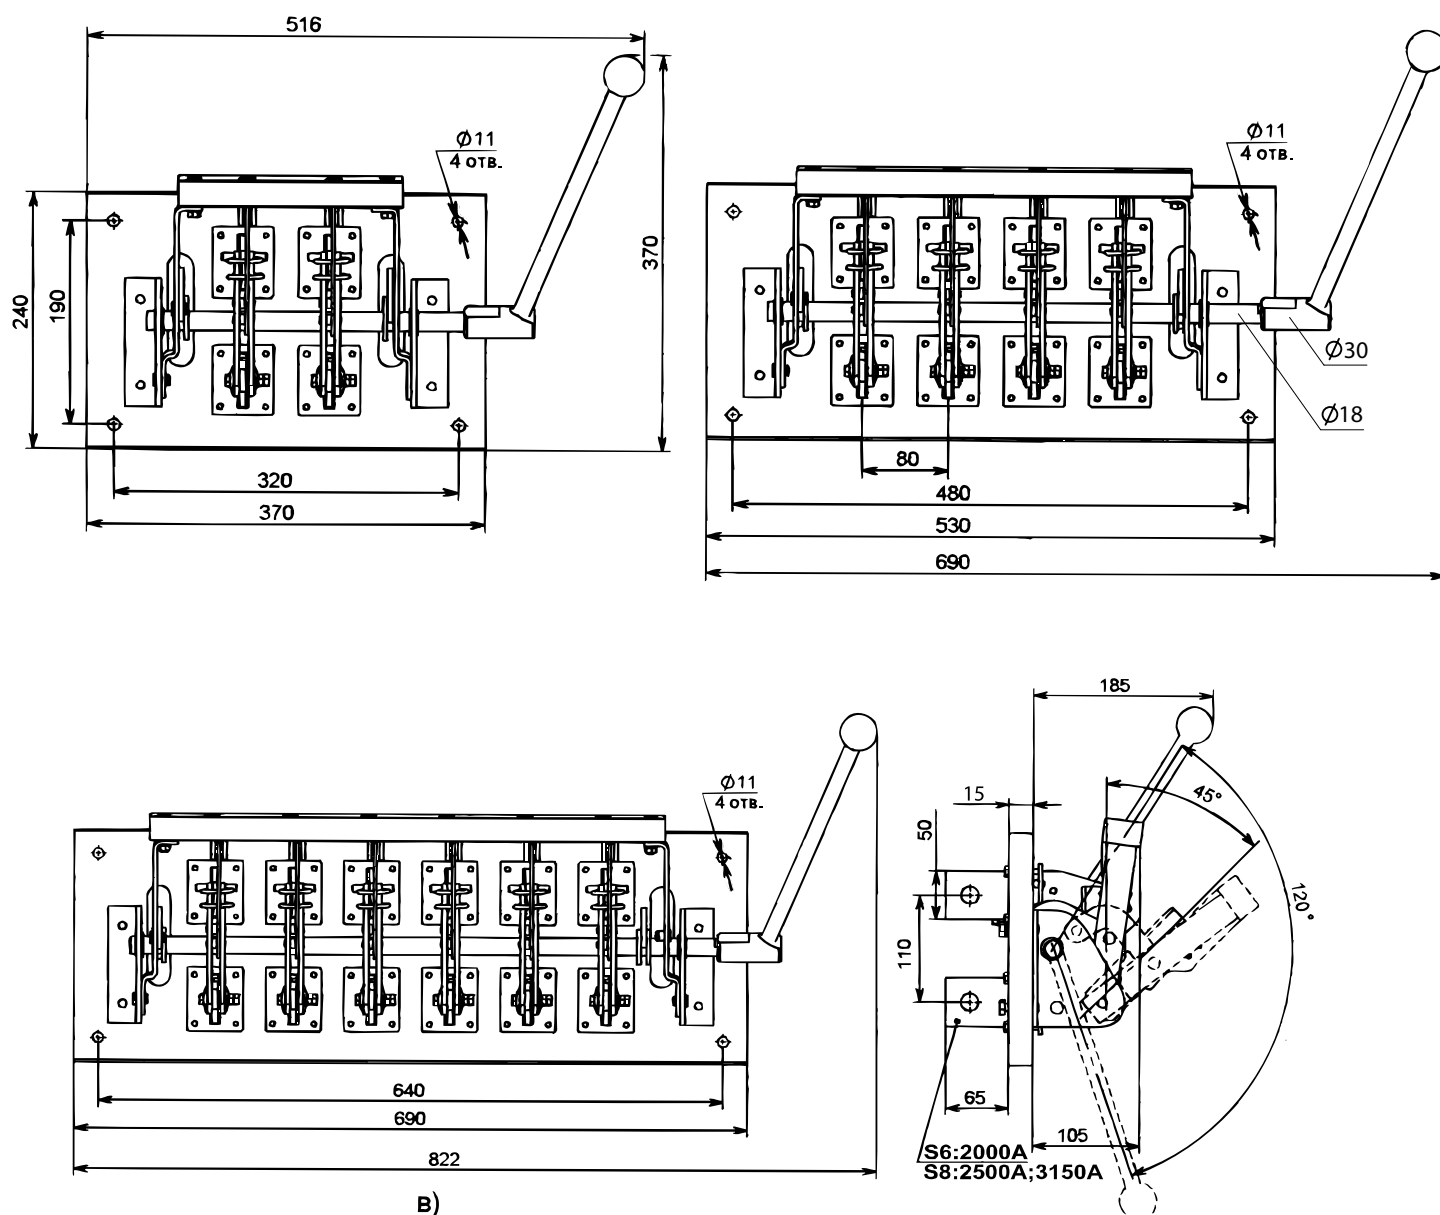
Разъединитель PE19 с боковой рукояткой, заднего присоединения шин
